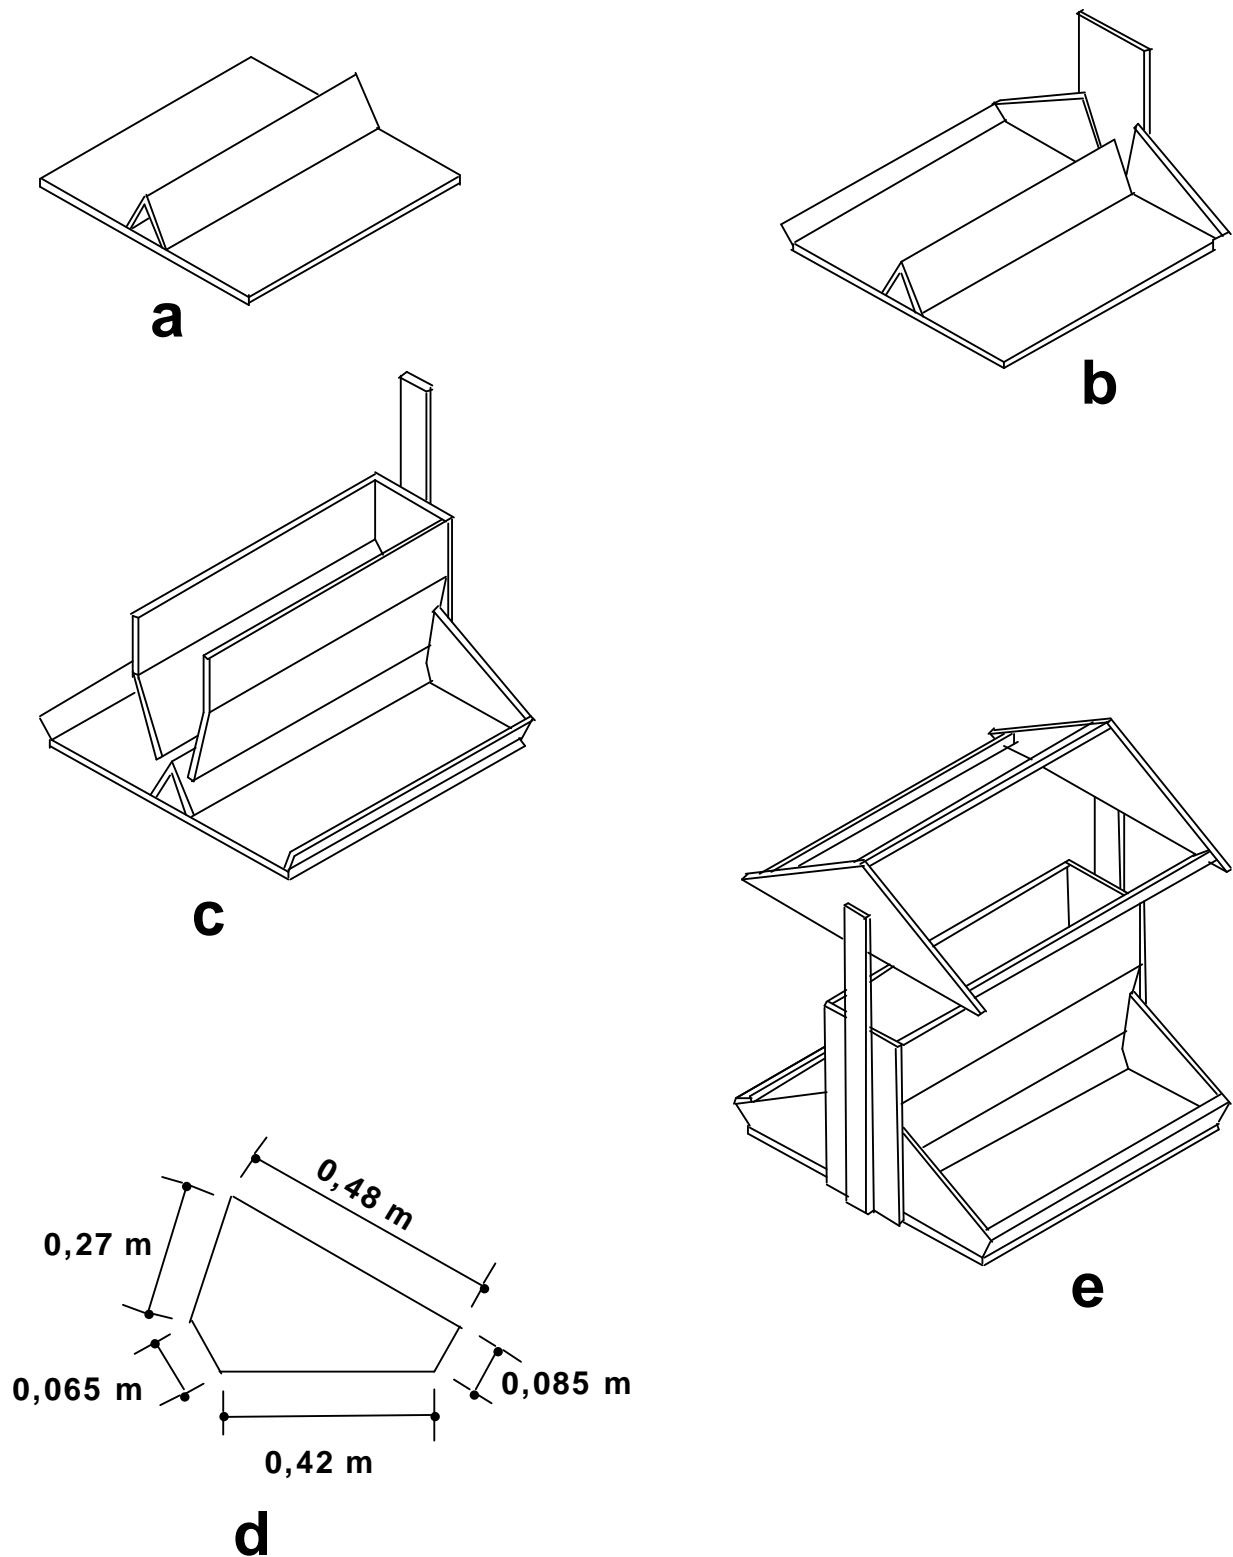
Detalhe da construção do comedouro: a) Direcionador de ração; b) Fixação da lateral e detalhe a; c) Depósito de ração e limiar do comedouro; d) Detalhe A; e) Visto geral do comedouro.
